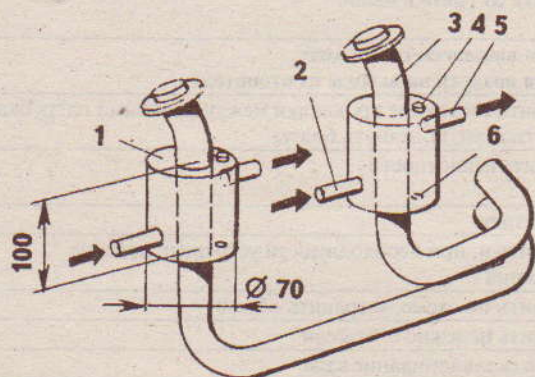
Установка резервуаров для нагрева антифриза на выпускных трубах: 1 - резервуар; 2 - впускной штуцер; 3 - труба; 4 - заливная пробка; 5 - выпускной штуцер; 6 - сливная пробка
